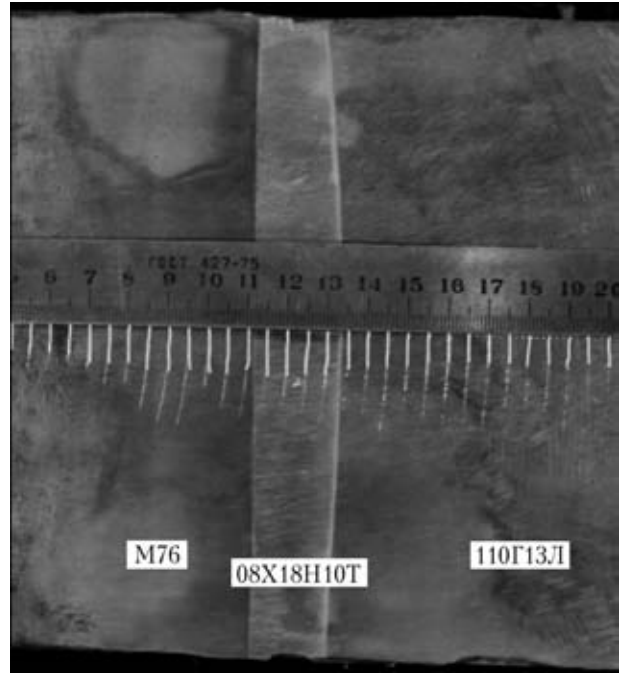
Вид сварного образца перед испытанием на статический изгиб
